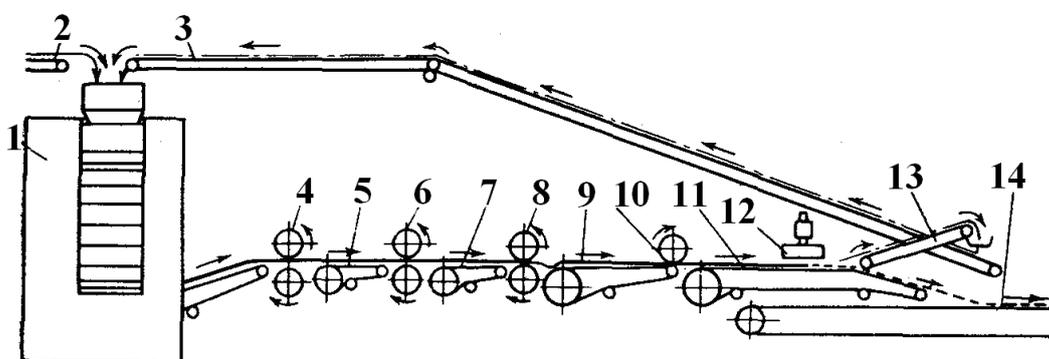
Принципиальная схема штамповально-режущего агрегата
